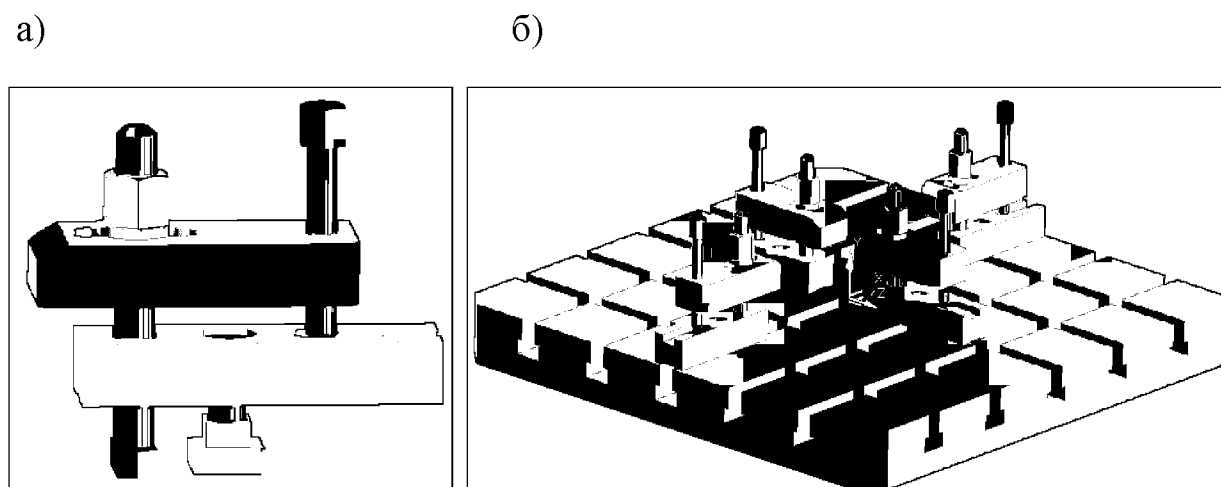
Основные этапы топологического синтеза трехмерной монтажной схемы паллеты многоцелевого обрабатывающего центра: а – компоновка типового сборочного узла элемента закрепления; б – размещение элементов закрепления по типовой схеме размерных связей
